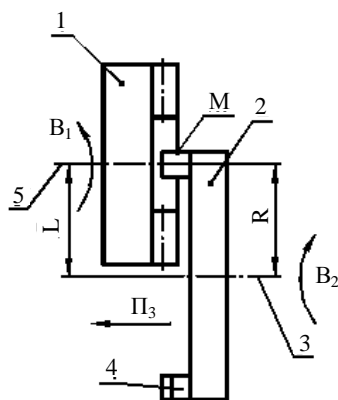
Базовая схема обработки ТЗК резцовой головкой
